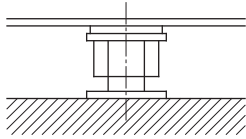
Nivellierschrauben auf der Fundamentoberfläche
